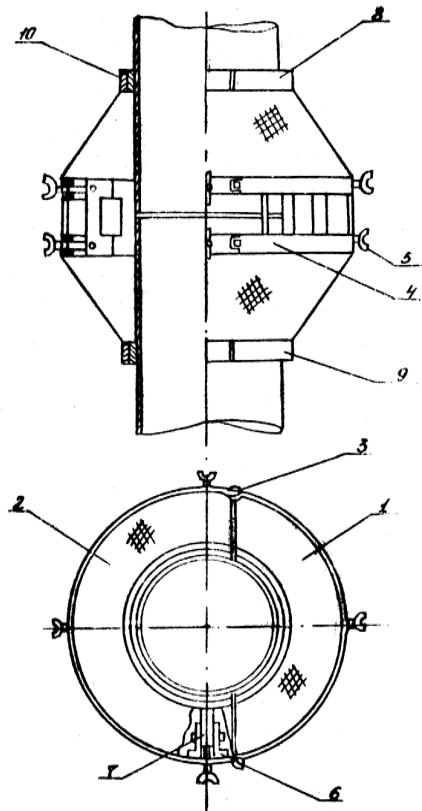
Приспособление для сварки трубопроводов в промышленных магнитных полях.
